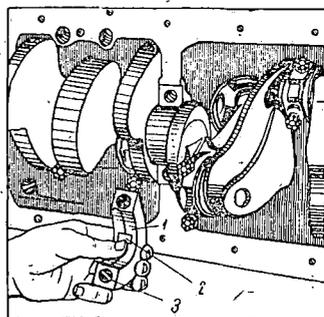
Проверка зазора в подшипнике коленчатого вала:
